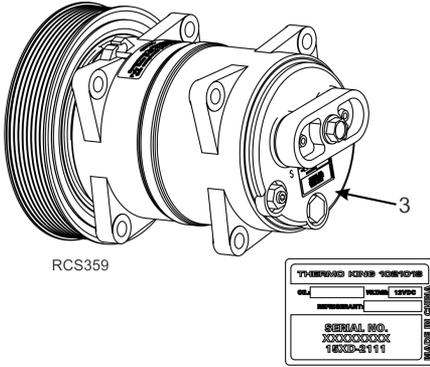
Места расположения серийного номера конденсатора и компрессора с резервным электроприводом
